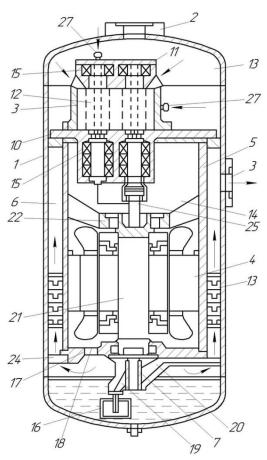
Герметичный вертикальный винтовой компрессор
